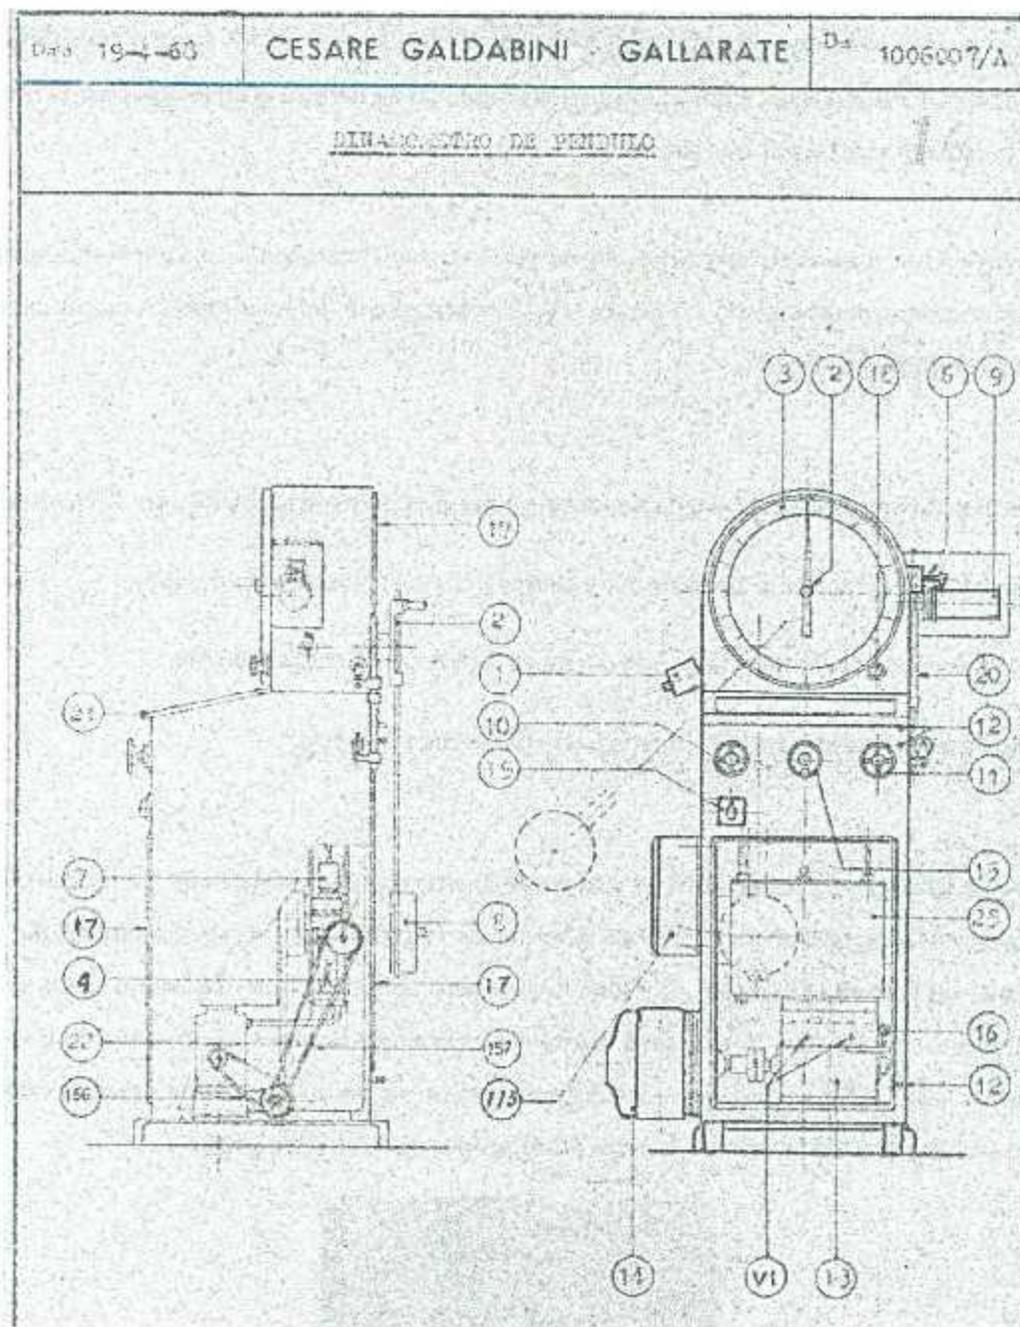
Vista isométrica de la máquina de ensayos universal, folio n° 16 -dibujo n° 1006007/A
